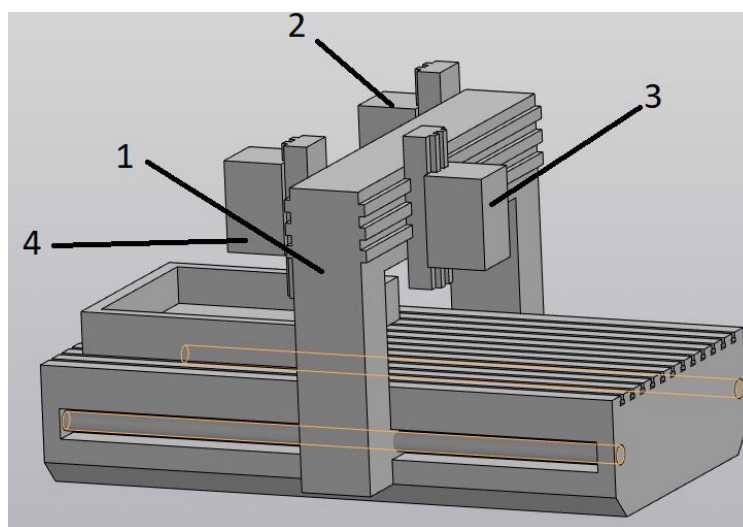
Общий вид установки: 1 – траверса, 2 – шпиндельная коробка, 3 – лазерная коробка, 4 – плазменная коробка
